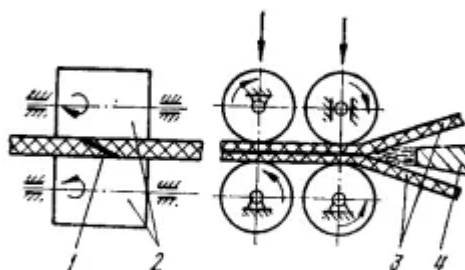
Схема сварки нагретым газом листов без присадочного материала
